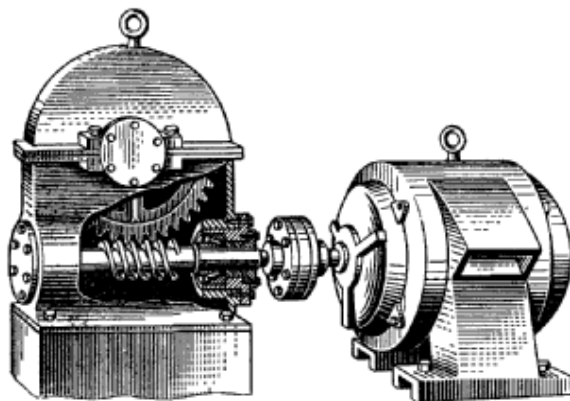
Привод «электродвигатель — червячный редуктор»
